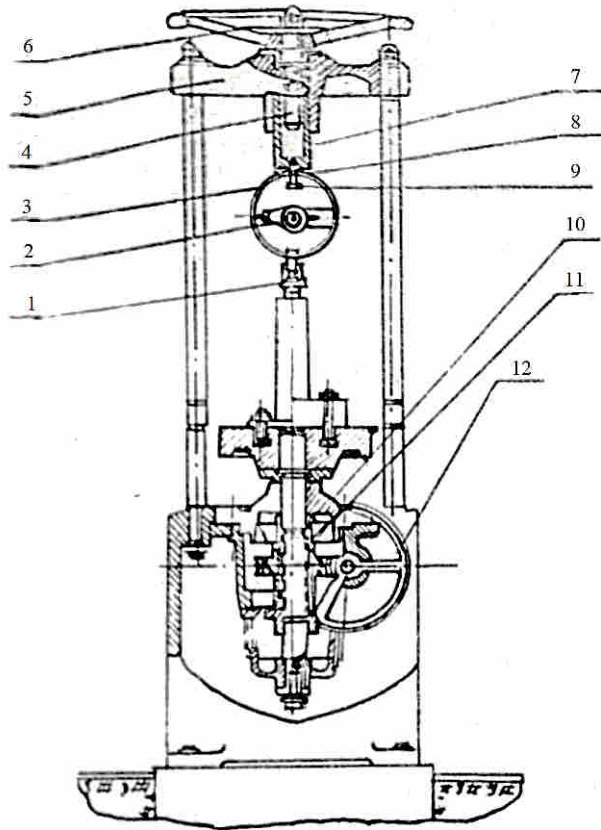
Машина для испытания на растяжение и сжатие ДМ-ЗОМ: 1 – наконечник; 2 – стрелочный индикатор; 3 – динамометрическое кольцо; 4 – винт; 5 – поперечина; 6 – маховик; 7 – ползун; 8 – верхний захват; 9 – болт; 10 – червячный редуктор; 11 – грузовой винт; 12 – маховичок
